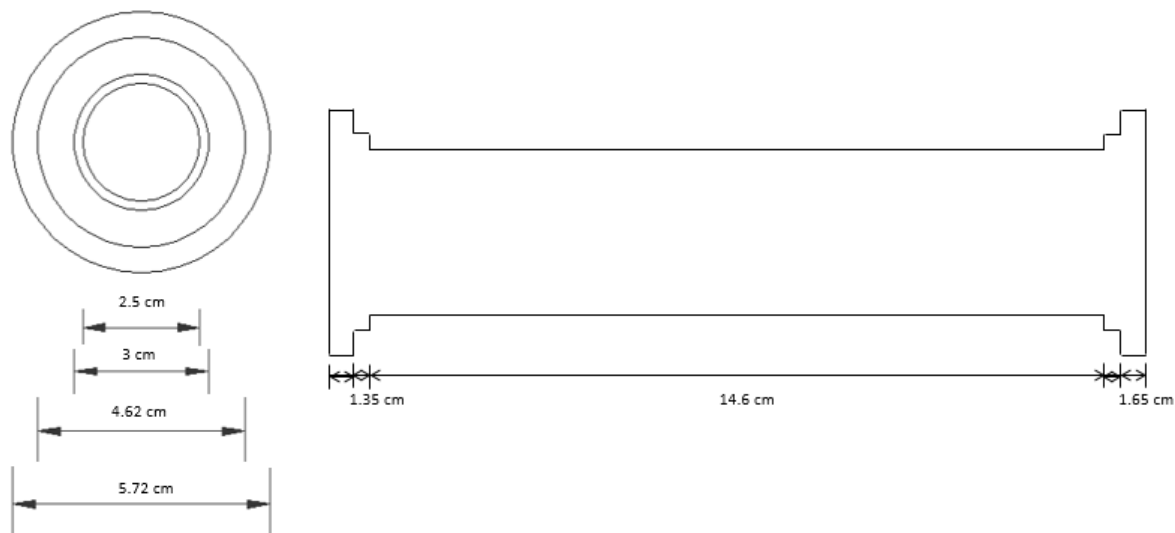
Vistas transversal y longitudinal de la columna de 25 mm de diámetro.
